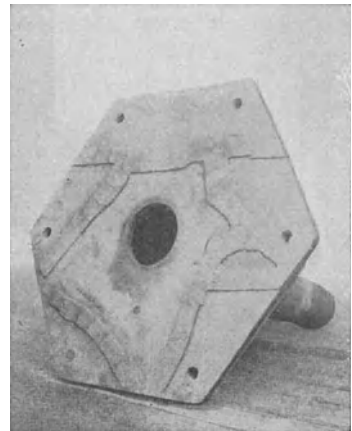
Ständerplatte nach der Schweißung.
